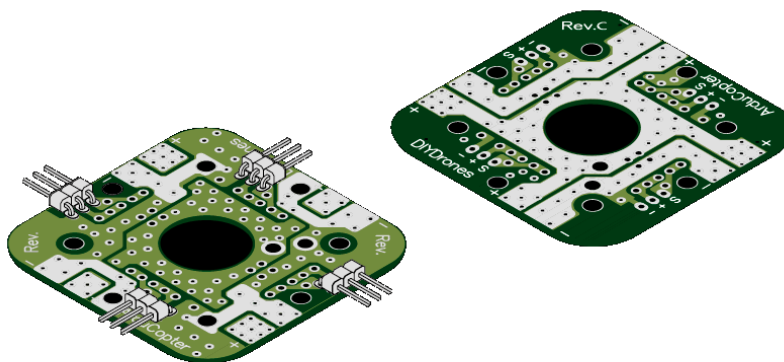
Imagem ilustrativa de como soldar os *header pins* [73]
